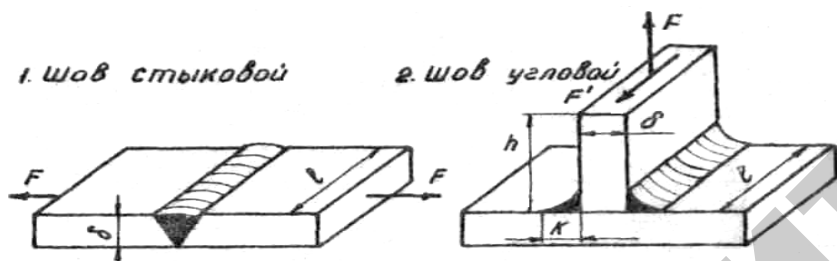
Аксонометрический эскиз сварных соединений
